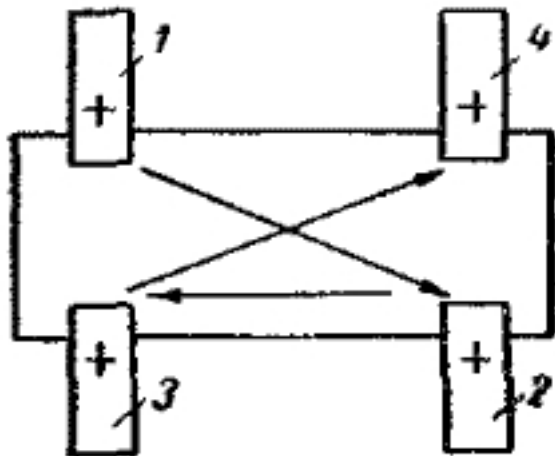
Последовательность закрепления детали несколькими прихватами.
